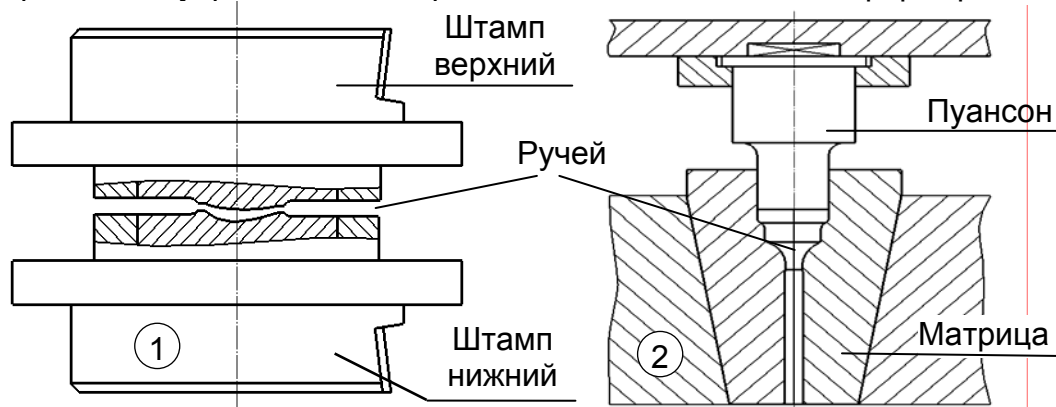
Эскизы элементов штампов для объемной штамповки лопаток: 1 – открытый калибровочный; 2 – закрытый для прямого выдавливания.
